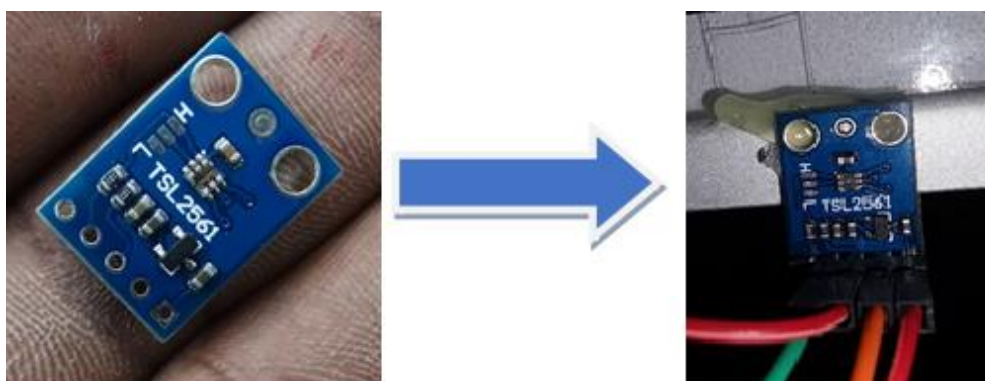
6): (TSL2561) Avant soudage et après soudage
